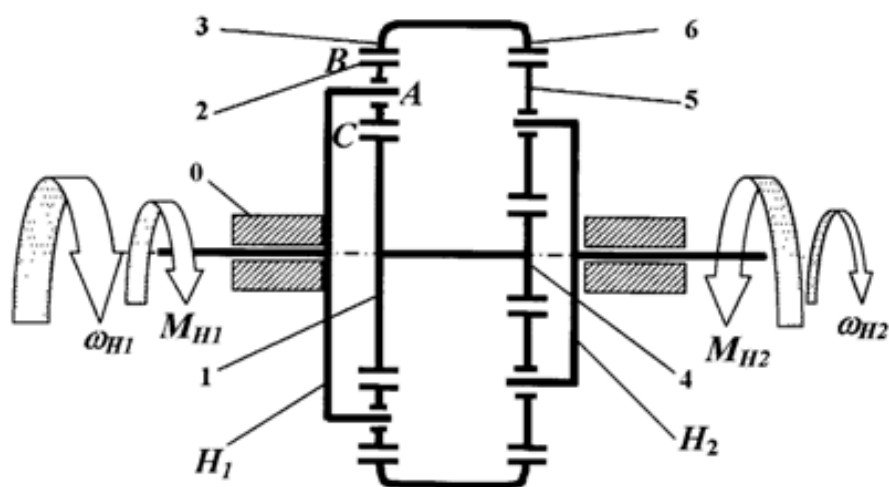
Схема ошибочной конструкции зубчатой бесступенчатой передачи
